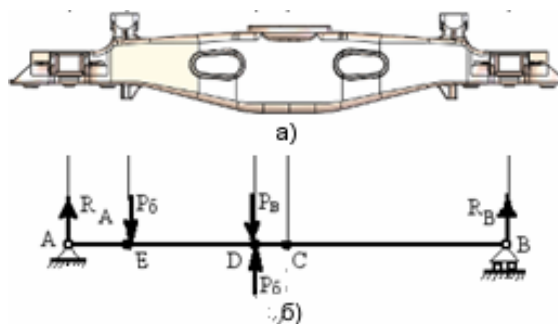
Расчетная схема для определения боковой нагрузки: а – надрессорная балка; б – расчетная схема
